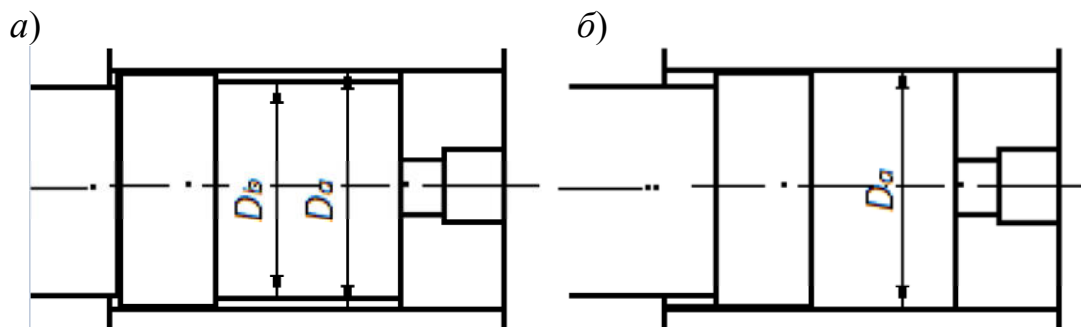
Первый этап прессования: распрессовка и осадка заготовки до начала истечения материала через матрицу: диаметр заготовки меньше диаметра пресс-блока (а), объем блока заполнен материалом заготовки (б). Пористость заготовки близка к пористости компактного материал
